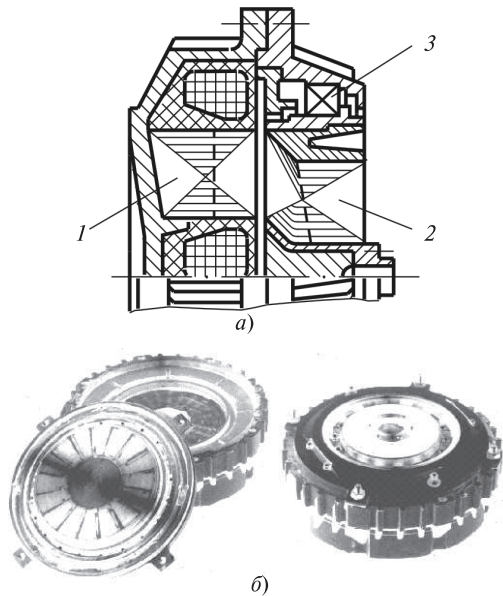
Конструктивная схема (а) и образцы (б) торцевого асинхронного двигателя для привода центробежного вентилятора: 1 – статор; 2 – ротор; 3 – подшипник
